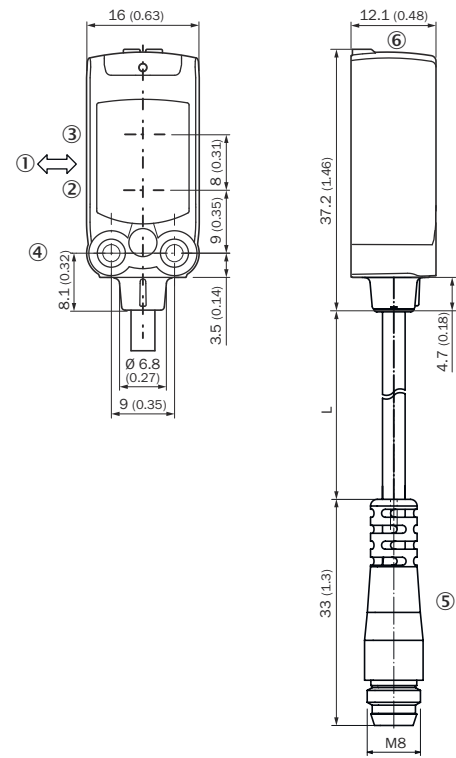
Disegno dimensionale, cavo con connettore maschio M8
